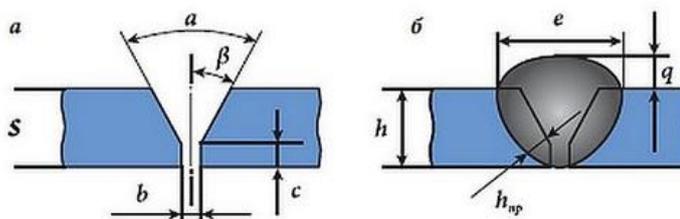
Геометрические размеры стыкового сварного соединения (до сварки и после сварки) подготовленных кромок под сварку (а): угол разделки кромок, угол скоса одной кромки, толщина свариваемого металла, зазор между стыкуемыми кромками, притупление кромки; выполненного шва (б): высота шва, ширина шва, глубина провара, усиление шва
